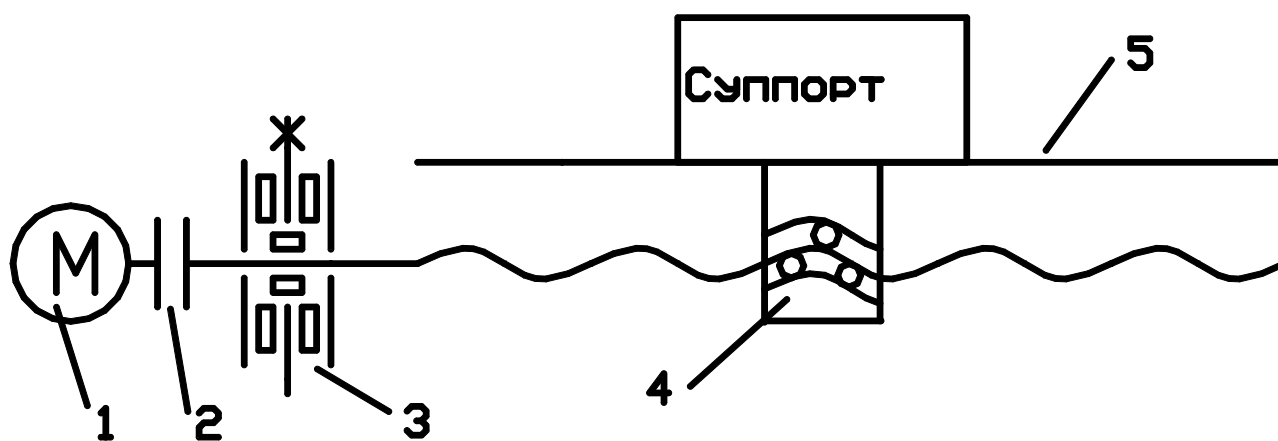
Схема проектируемого привода подачи станка с ЧПУ: 1 – двигатель постоянного тока, 2 – соединительная муфта, 3 – комбинированный подшипник, 4 – передача винт – гайка качения, 5 – неподвижная направляющая
